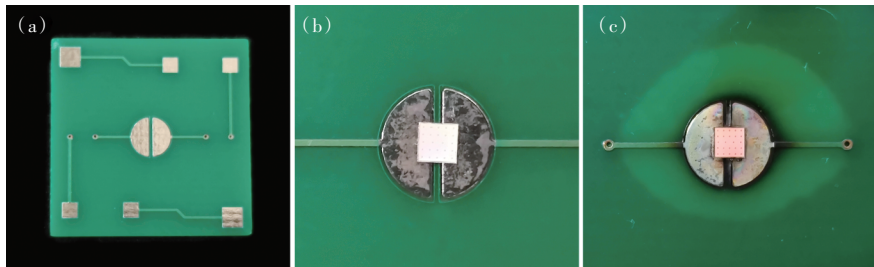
(a)普通 PCB 基板实物图;(b)封装 LED 芯片后普通 PCB 基板局部放大图;(c)700 mA 时,普通 PCB 基板失效图。
